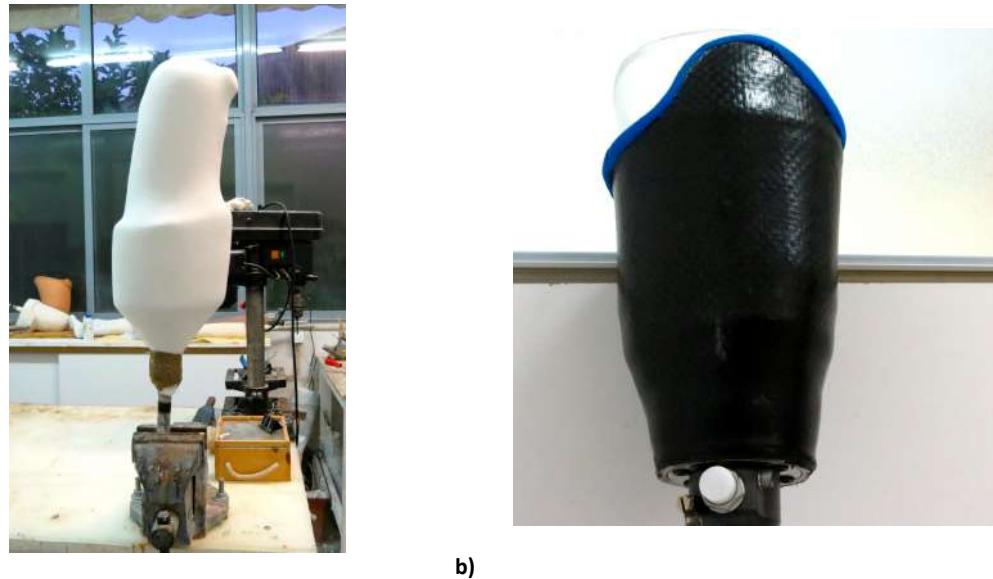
Molde pronto para laminagem a) e encaixe final TSB em fibra de carbono
